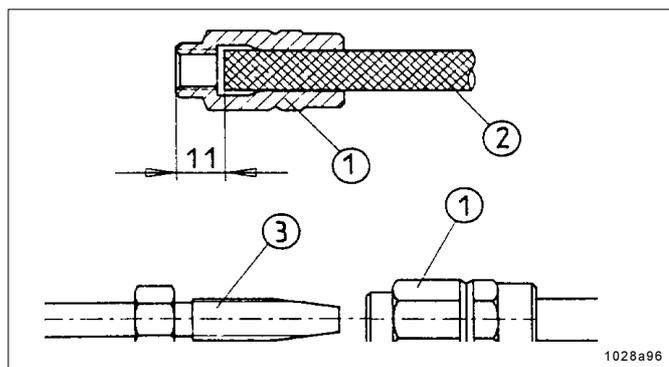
Prémontage des douilles filetées et des embouts pour tuyau sur la conduite principale
